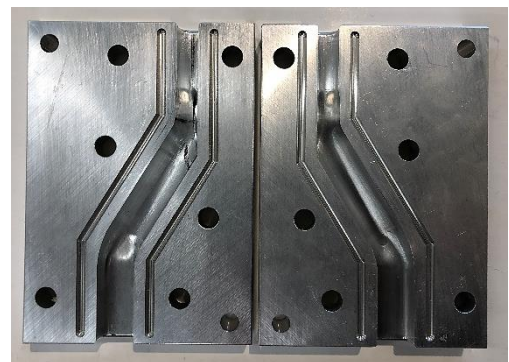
Moule en aluminium pour fibres pré-imprégnées
